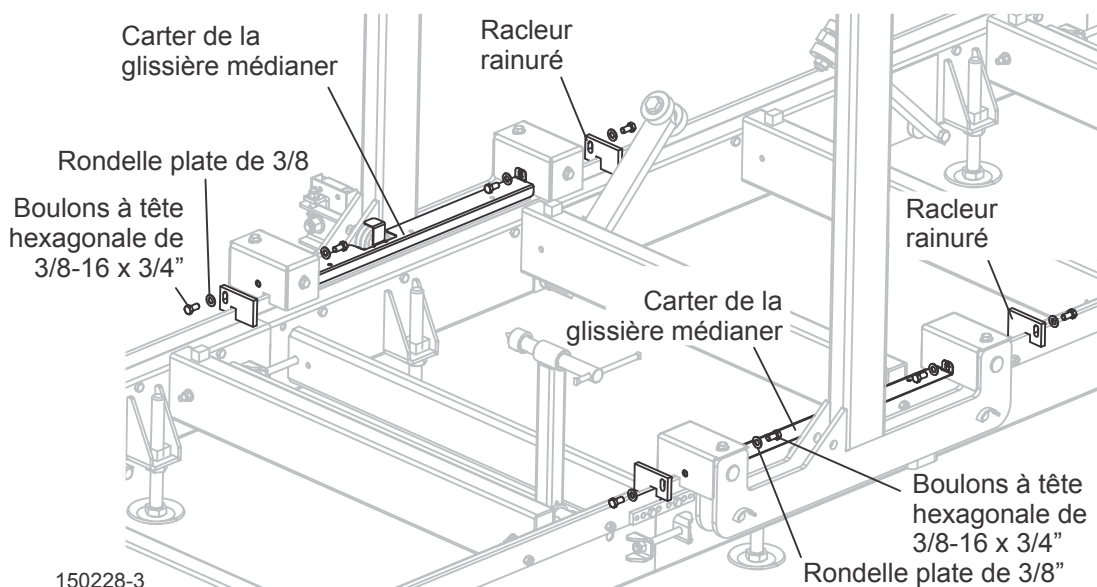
LT15 WIDE HEAD SEULEMENT
